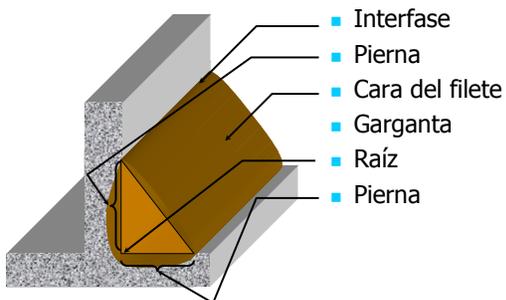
Nomenclatura empleada en las uniones soldadas
